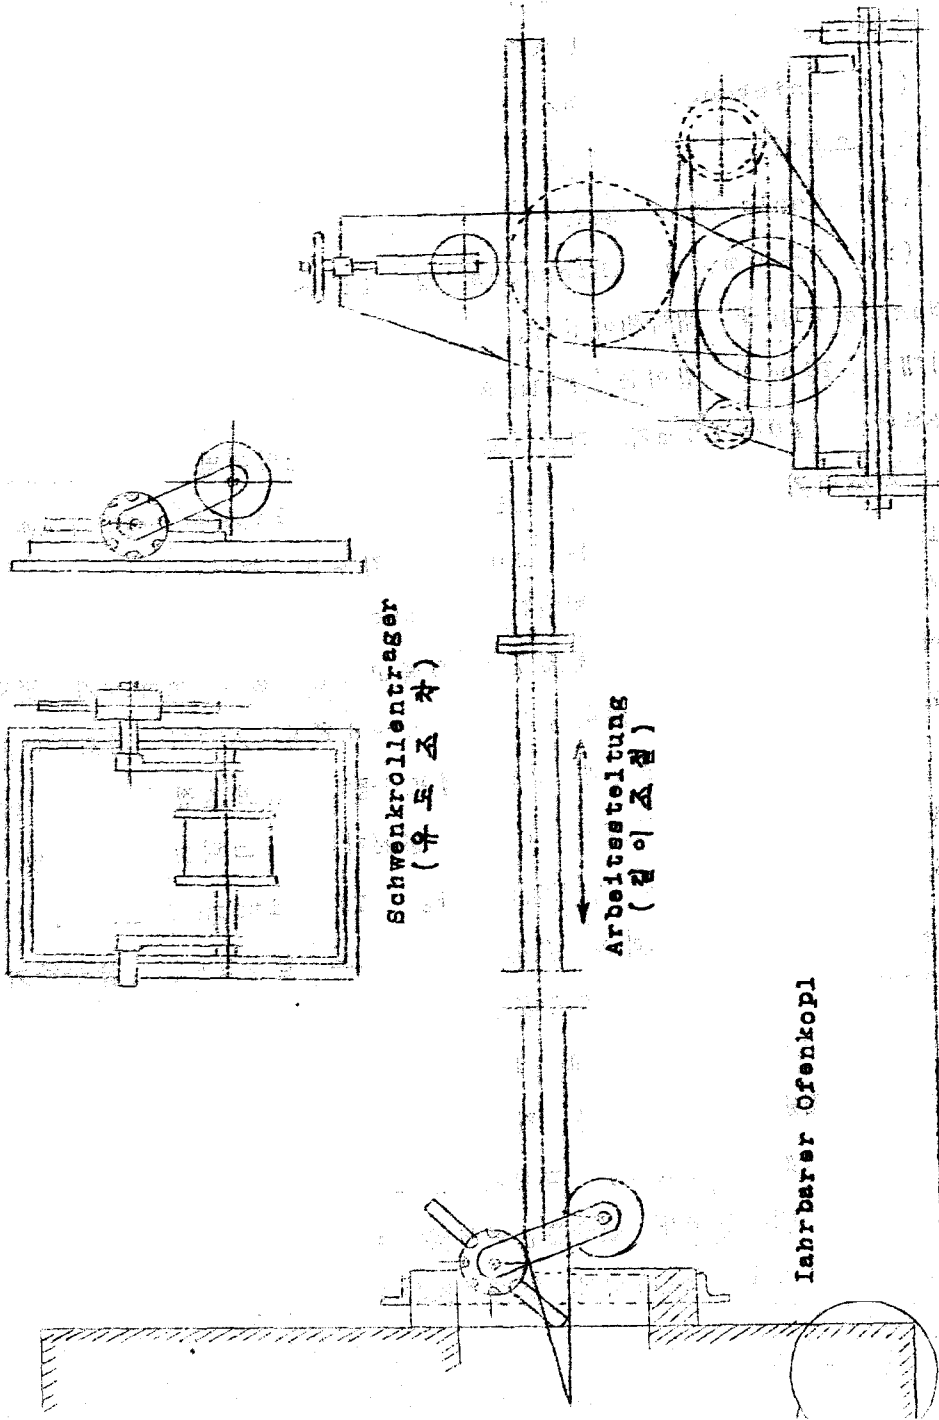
Brodmaschiezum Entfernen von Schlackenringenin
